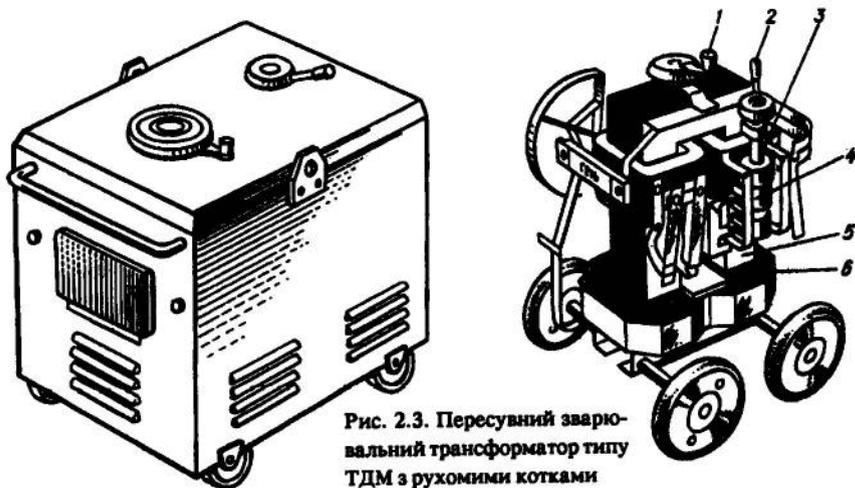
Пересувний зварювальний трансформатор типу ТДМ з рухомими котками
